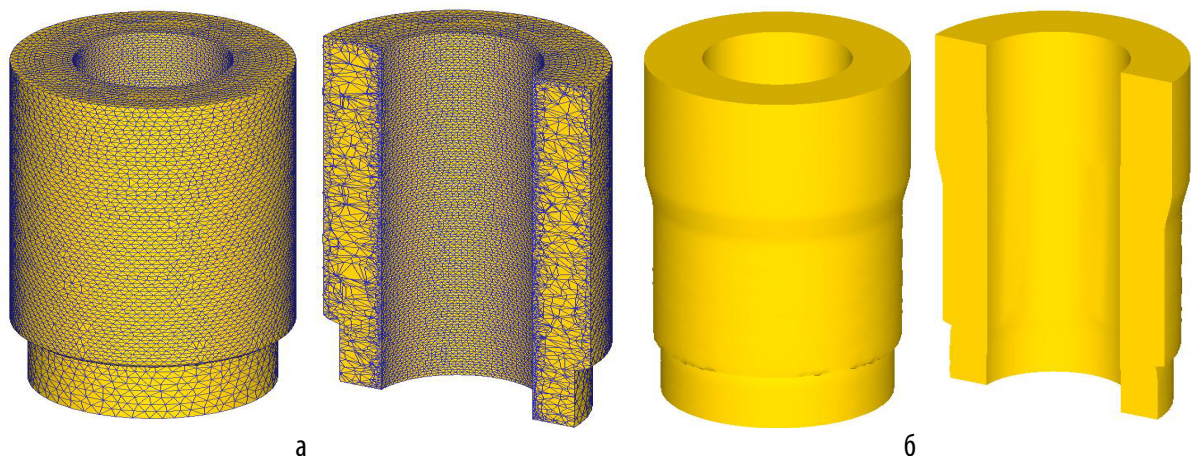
Формообразование полигонального профиля канала ствола волочением (обжатием) в гладкой конической матрице: а – заготовка с КЭ сеткой; б – деталь после деформации
